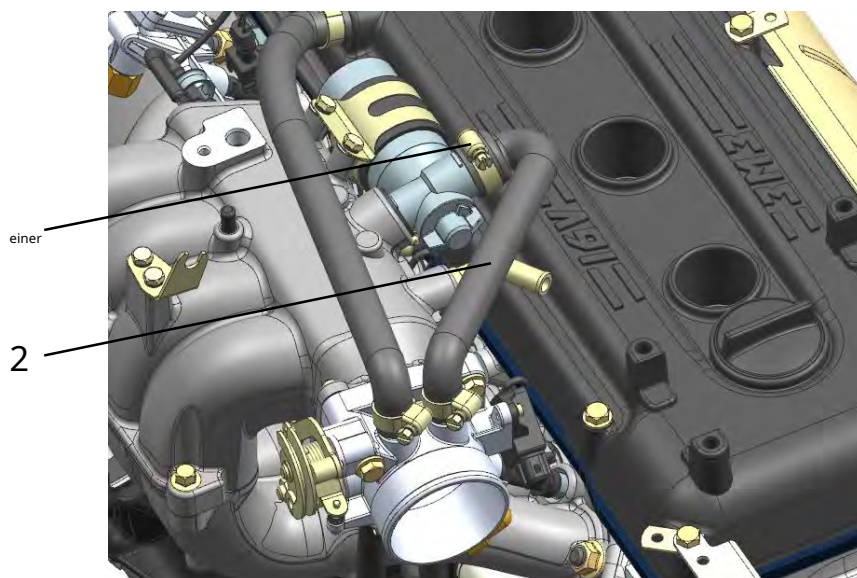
Installation des Leerlaufluftsteuerschlauchs:
